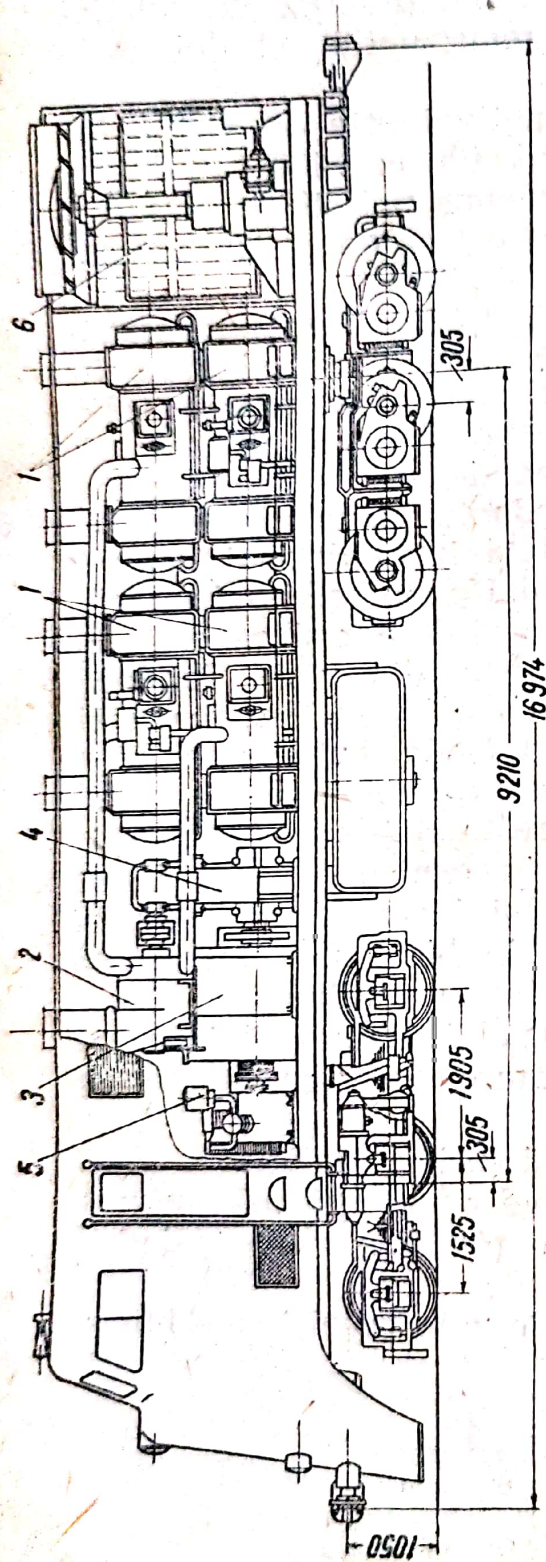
Locomotivă sovietică acționată prin generatoare de gaze cu pistoane libere cu transmisie electrică.
